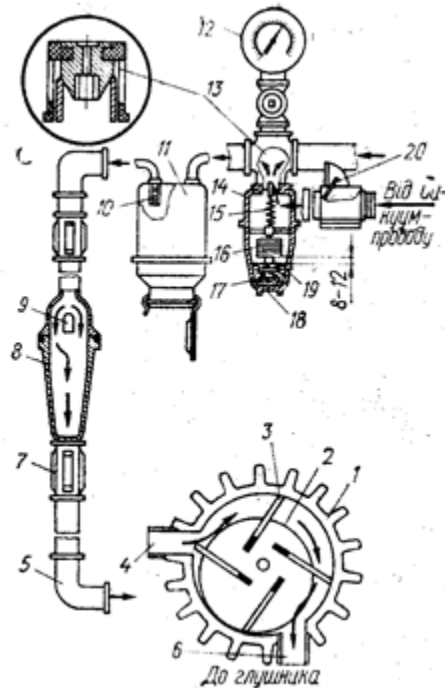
Вакуумна установки УВУ-60/45 [1]: 1 – корпус насоса; 2 – ротор; 3 – лопатка; 4 – впускний патрубок; 5 – коліно; 6 – випускний патрубок; 7 – муфта; 8 – запобіжник; 9 – зворотний клапан; 10 – клапан-поплавець; 11 – вакуумний балон; 12 – вакуумметр; 13 – клапан регулятора; 14 – корпус вакуумрегулятора; 15 – пружина; 16 – вага; 17 – демпферний диск; 18 – стакан; 19 – олива; 20 – індикатор витрат.
